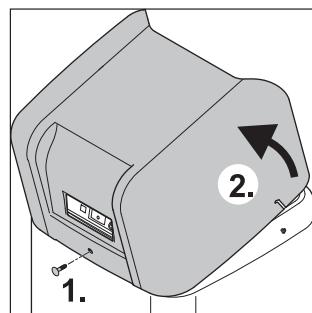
Schraube herausdrehen und Abdeckhaube hinten entriegeln.
